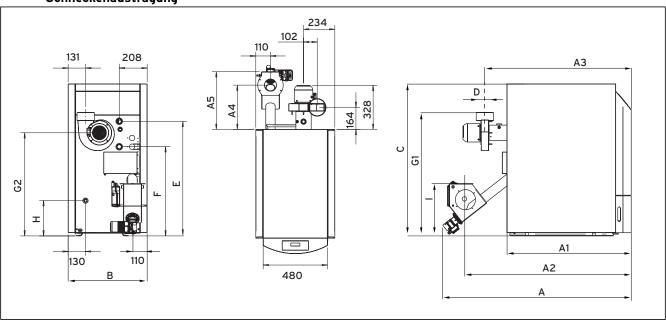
Abmessungen: Pelletkessel mit Schneckenaustragung
